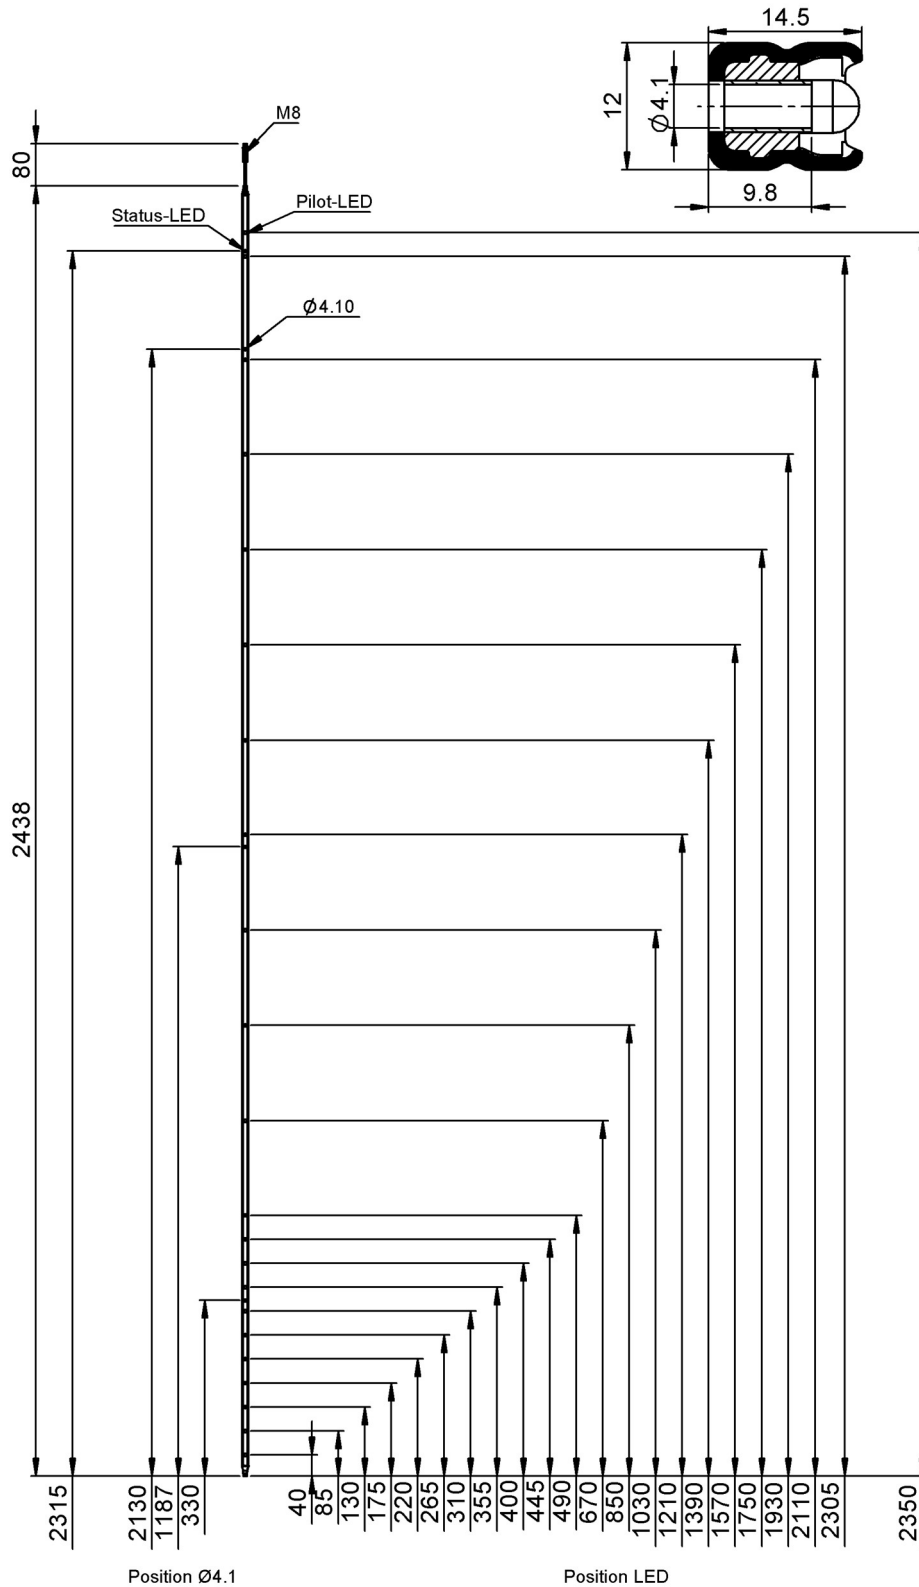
RAY-LG 3522 Dimensionen (mm)
